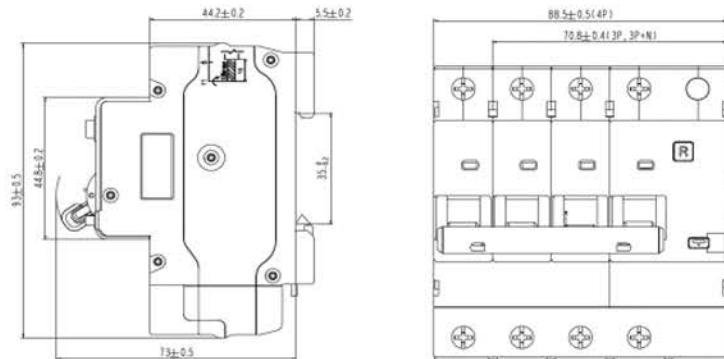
Установочные и габаритные размеры ДИФ-103 6кА 3P, 3P+N
